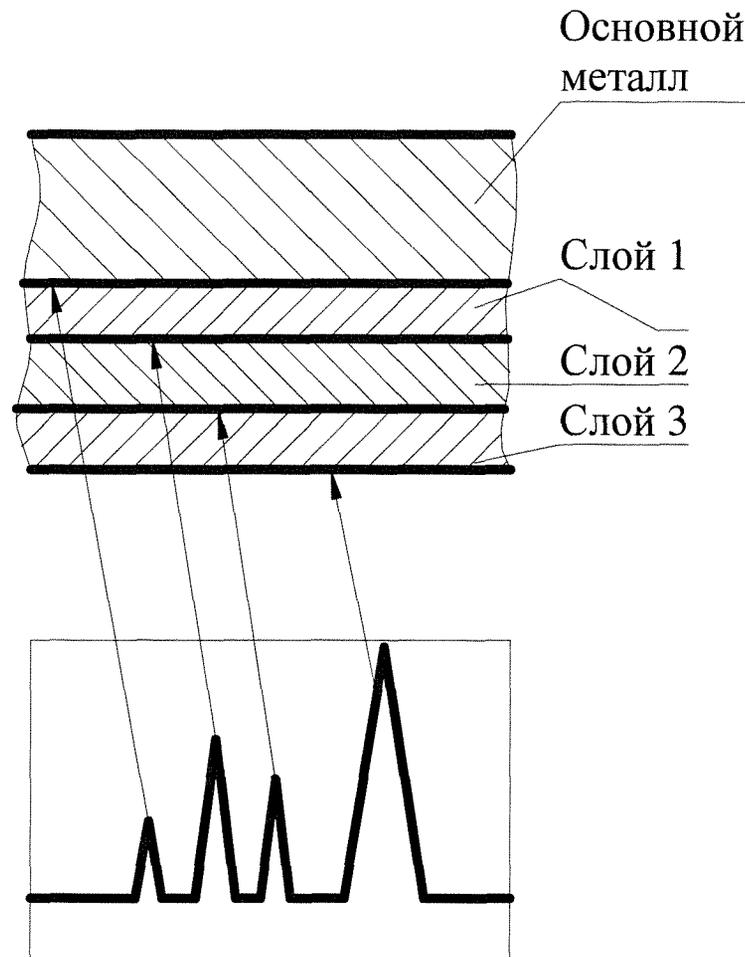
Отражения от зоны сплавления наплавки с основным металлом и границ слоев наплавки
